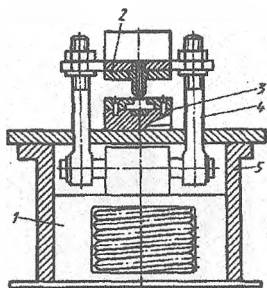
Приспособление для пробивки отверстий на ремешках
